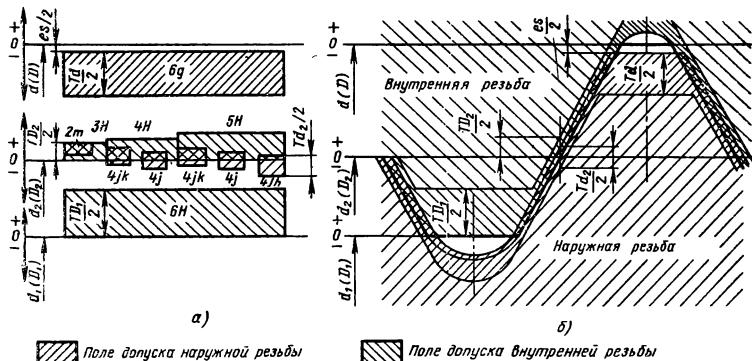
Схемы расположения рекомендуемых при переходной посадке полей допусков наружной и внутренней резьбы (а) и верхней части профиля резьбы с полями допусков по всем диаметрам (б)
